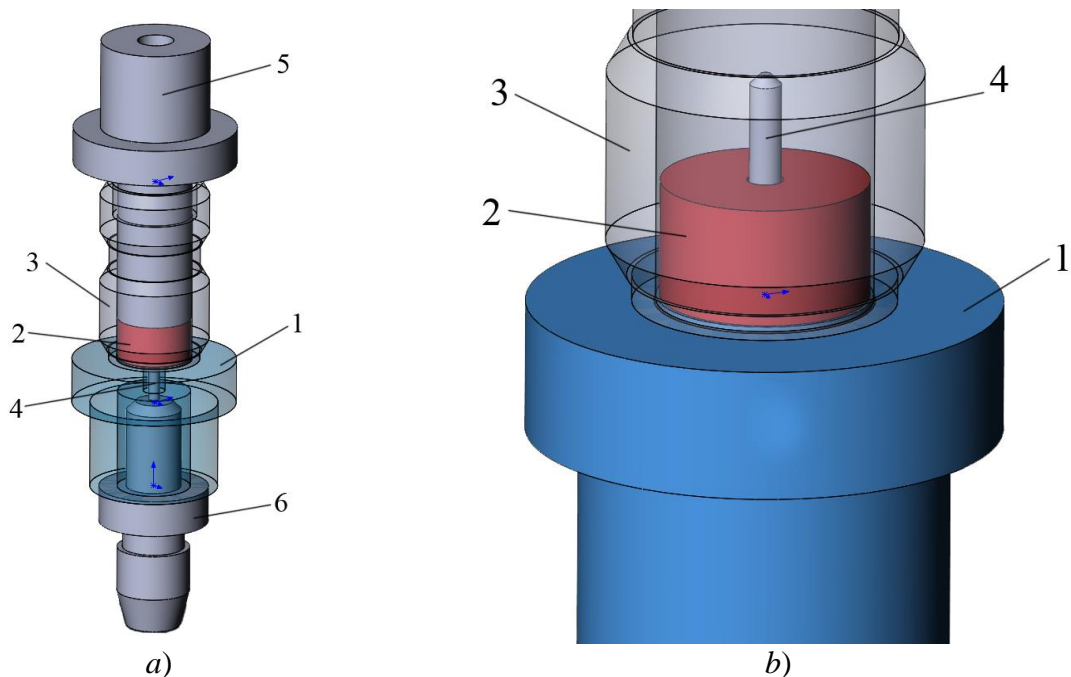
Приспособление для спаивания СРГ, *a* – сборка соединителя на опоре, *b* – с вставленным упором:
